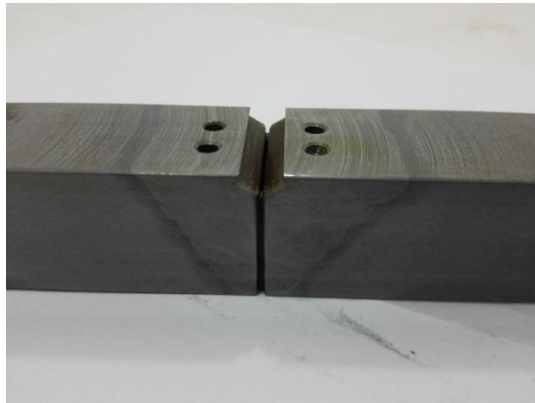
Localização da região da junta soldada mostrando onde o entalhe foi posicionado. Fonte: próprio autor
